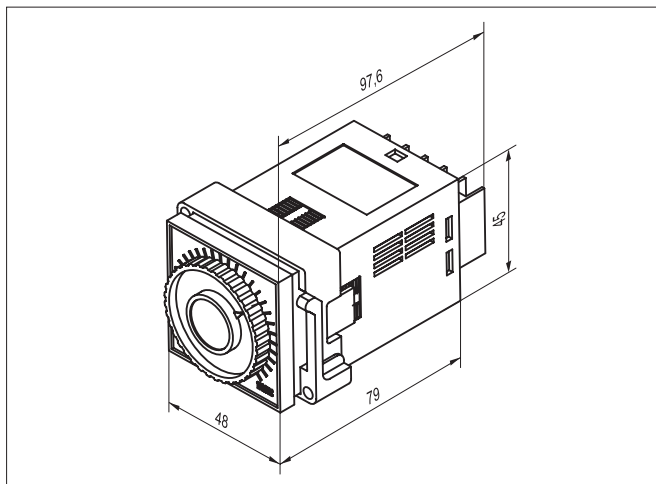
Габаритный чертёж ОВЕН ТРМ502
